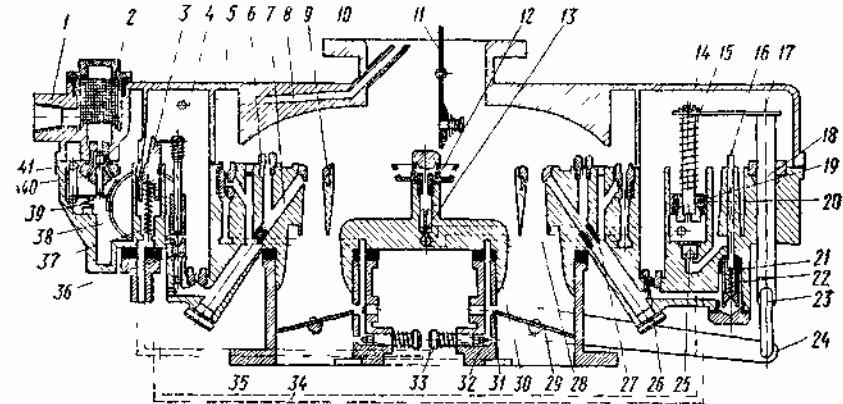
Карбюратор К-88 двигателя ЗИЛ-130
